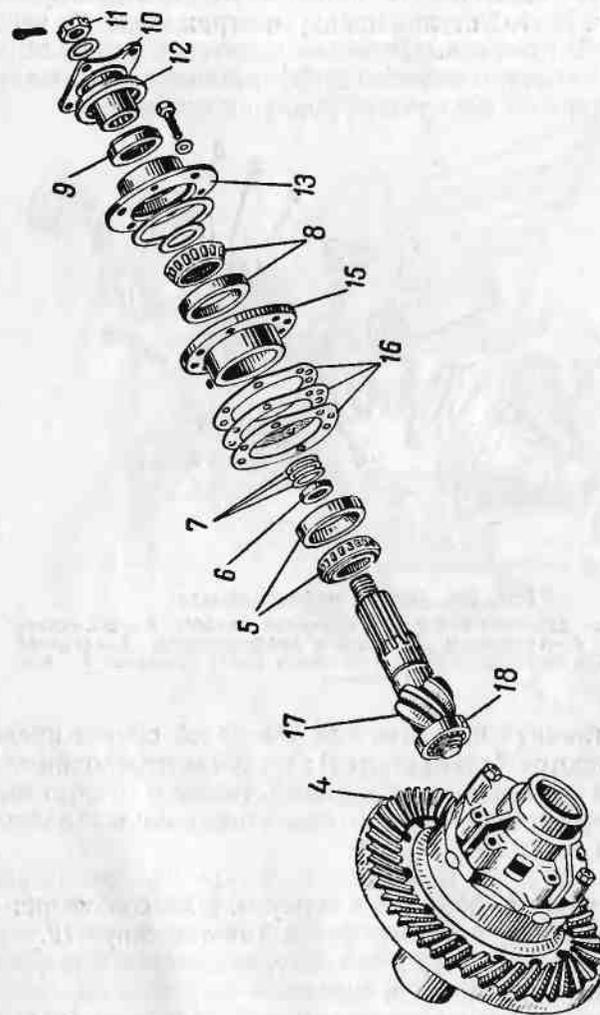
Детали главной передачи (обозначение деталей то же, что на рис. 118)
